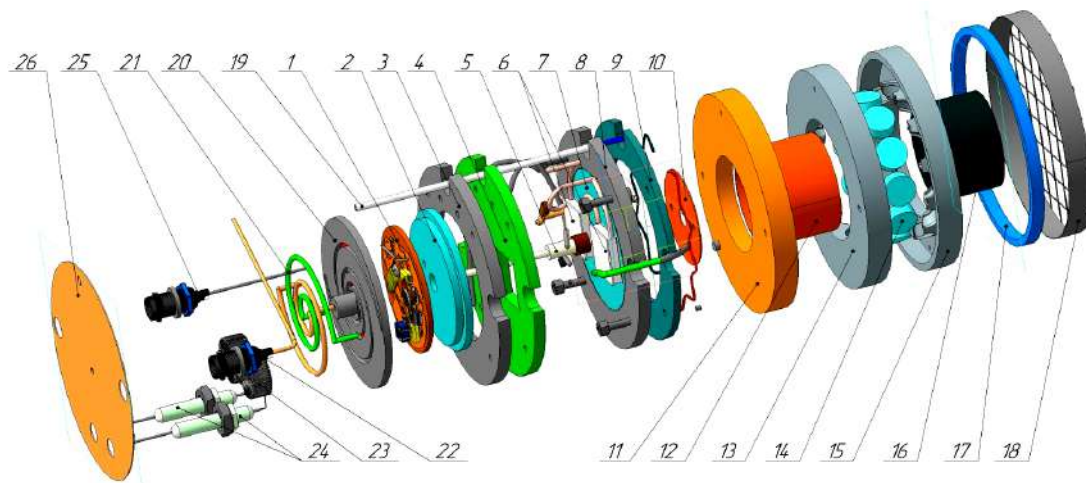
Разнесённый вид конструкции прототипа УМД МК:
